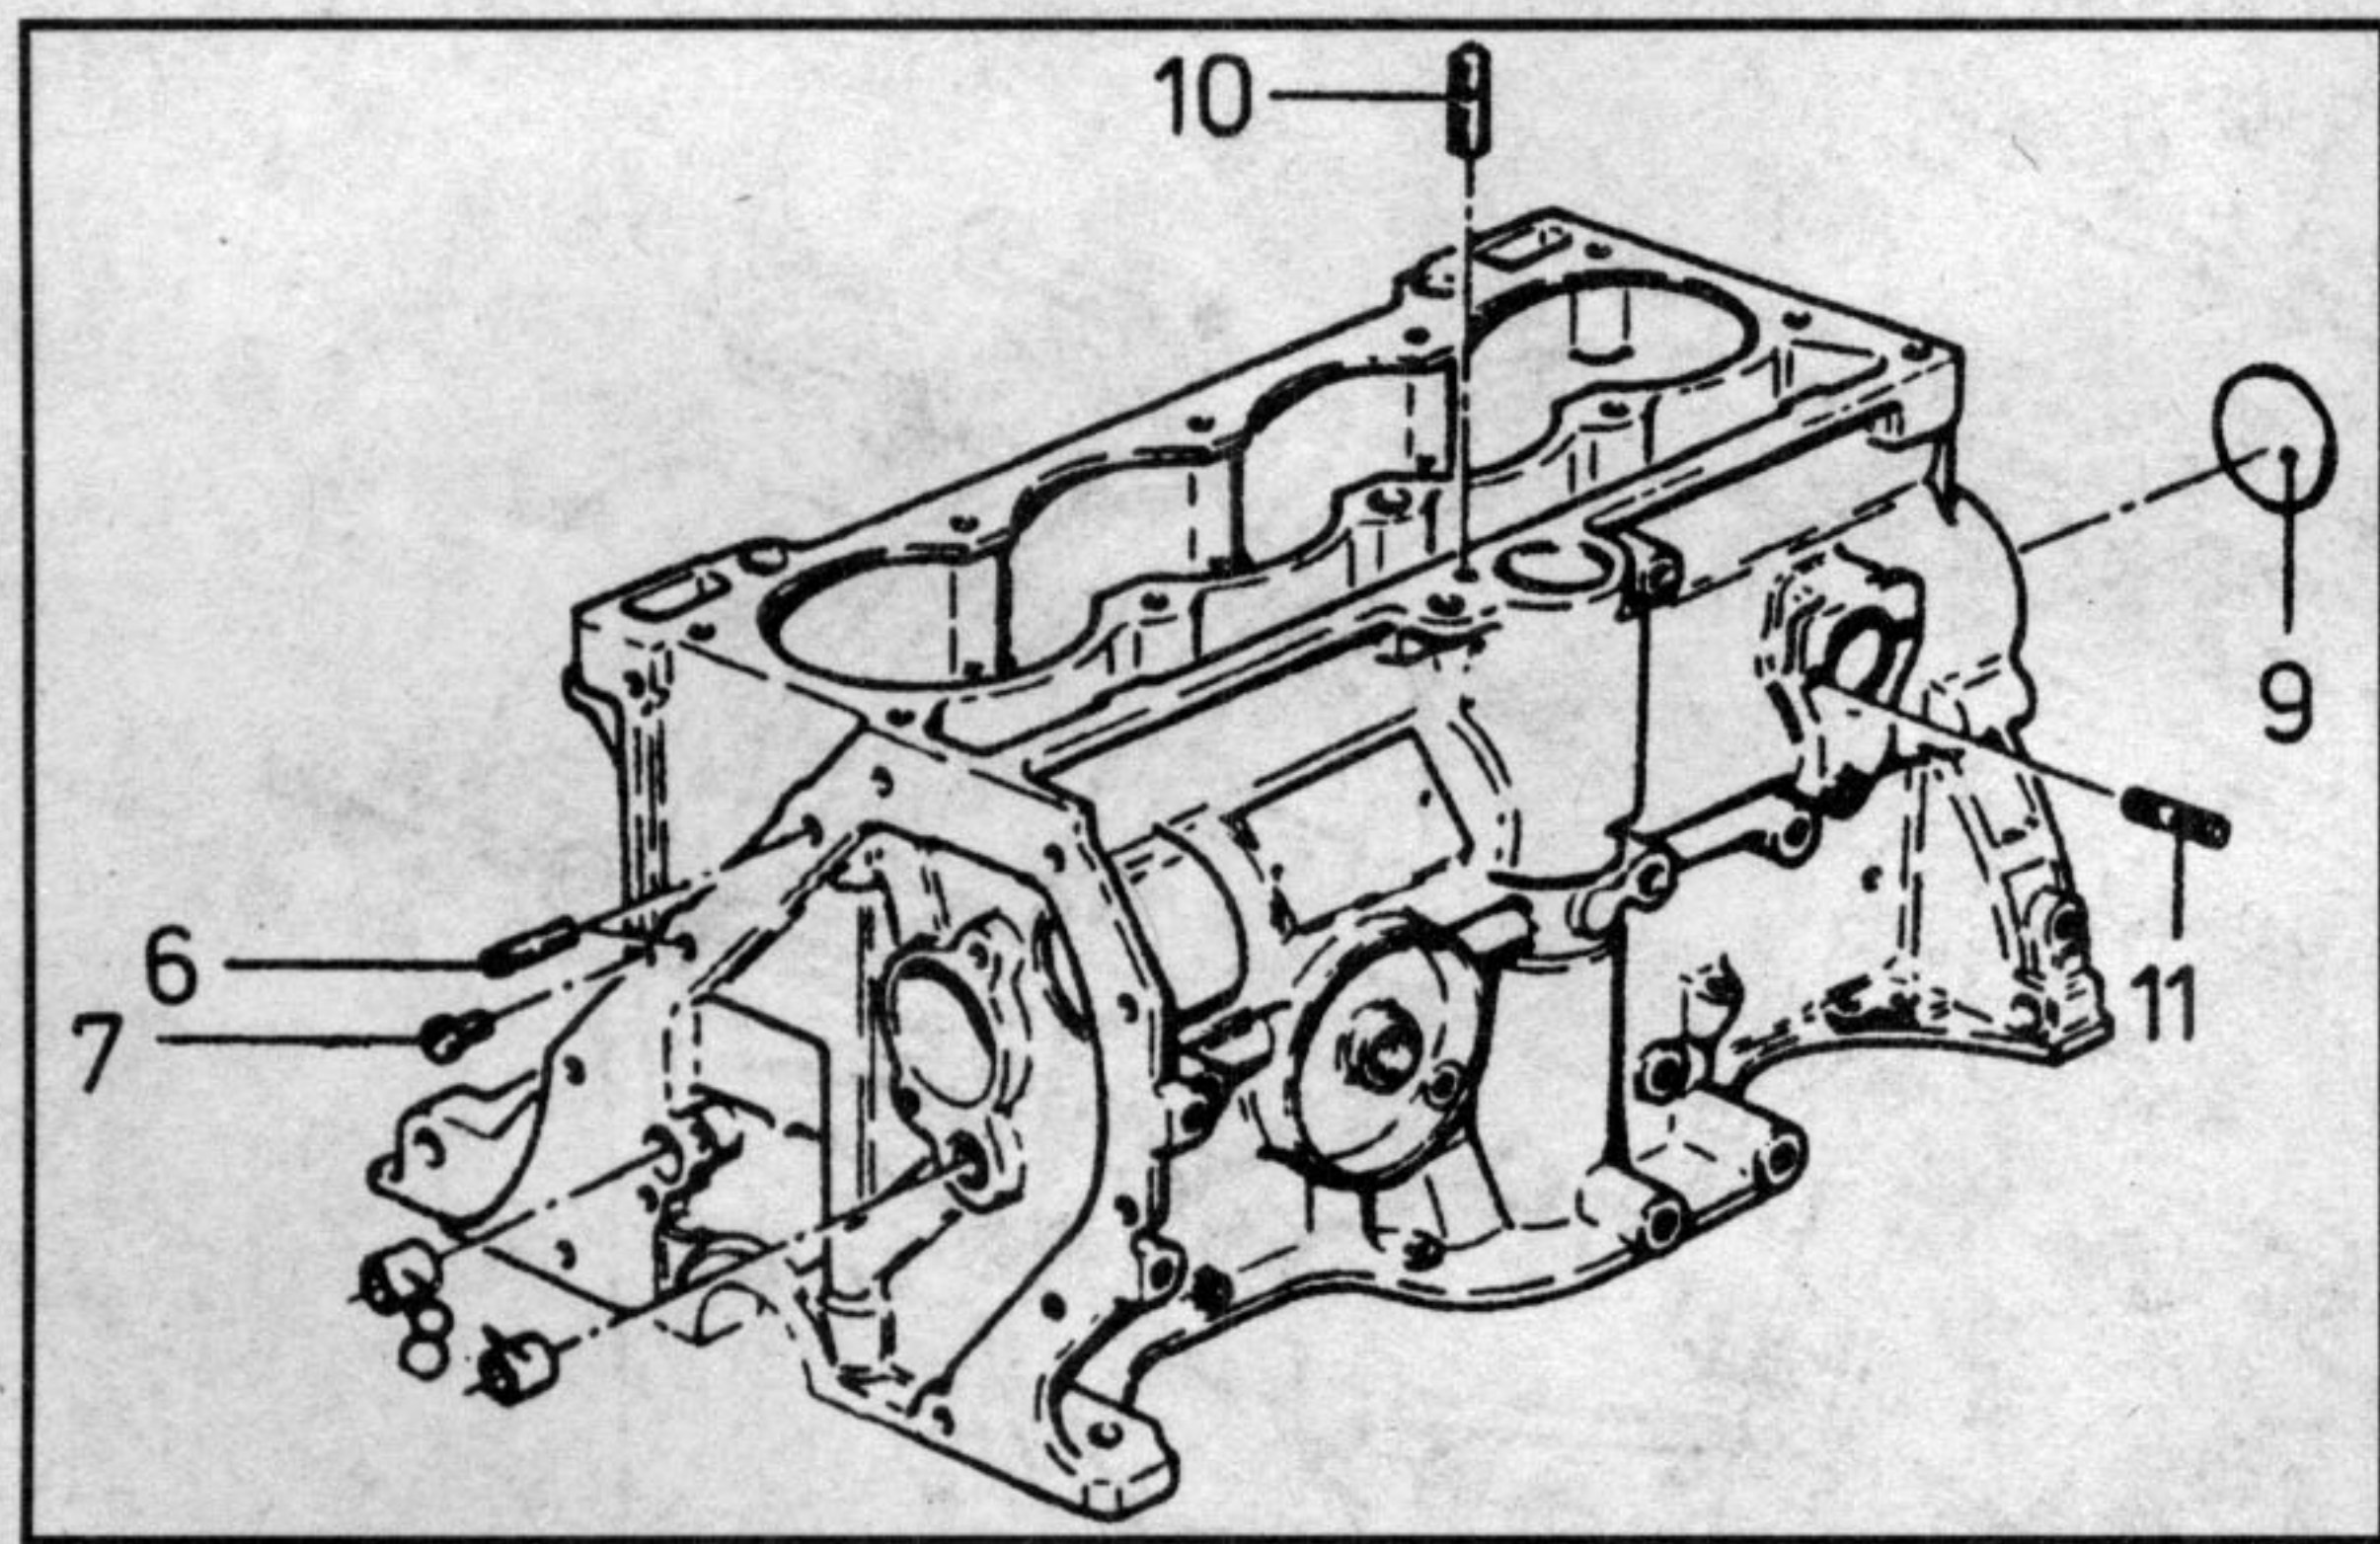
Элементы крепления к блоку цилиндров двигателя В13/В14
